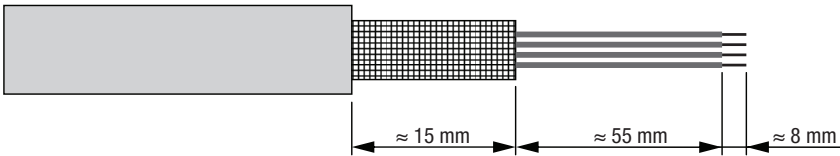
Confección del cable para el módulo de bornes MK 301
